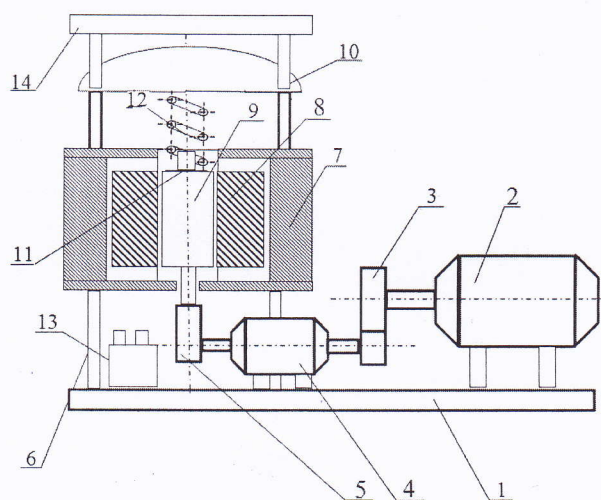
Схема пристрою для вібро-магнітно-абразивної обробки різальних пластин із ПКНБ
